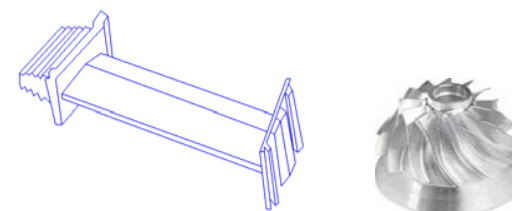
Примеры деталей с криволинейными поверхностями
